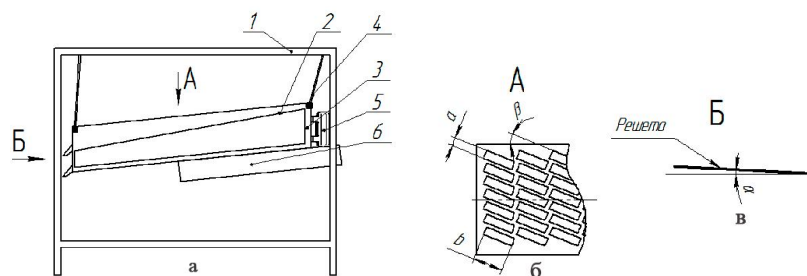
Схема лабораторной установки: а – общий вид; б – вид А; в – вид Б; 1 – корпус; 2 – решето прямоугольной формы; 3 – решетный стан; 4 – шарнирные тяги; 5 – электродвигатель; 6 – привод
